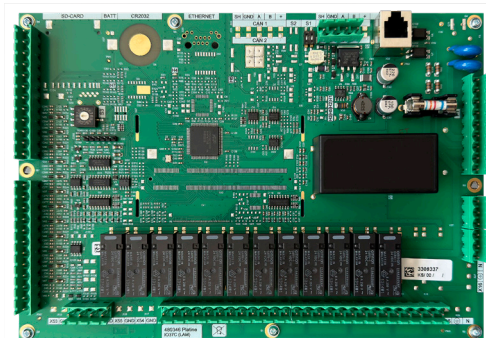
Unité de régulation hydraulique AHC 310x170x80 mm
